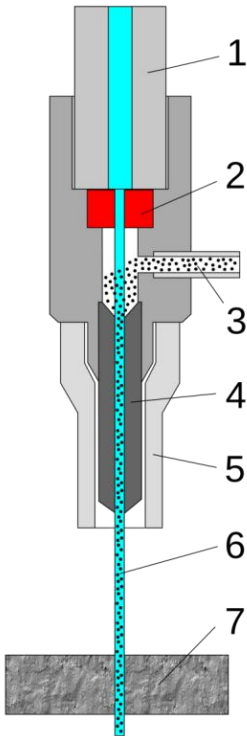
Схема установки для гідроабразивного різання:
